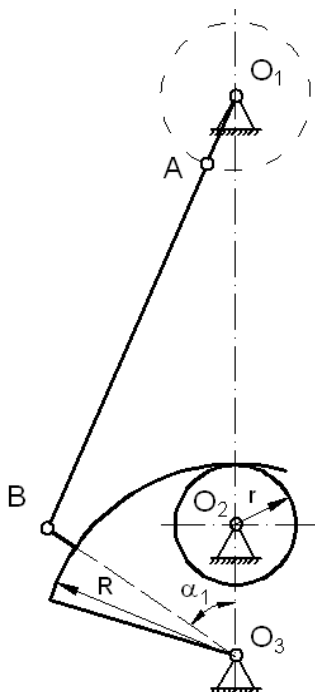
Кінематична схема приводу човникового пристрою з використанням зубчатої передачі внутрішнього зачеплення
